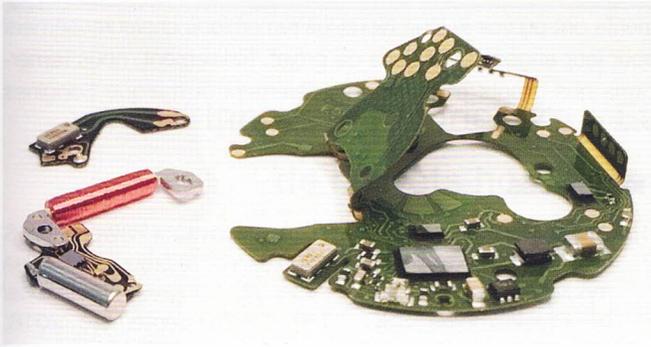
Comparaison des PCB de mouvements trois aiguilles ETA. En haut à gauche: PCB rigide, mouvement Fox. En bas à gauche: PCB rigide, mouvement MinETA. A droite: PCB flexible (FPC), mouvement NTC 3 aiguilles.
